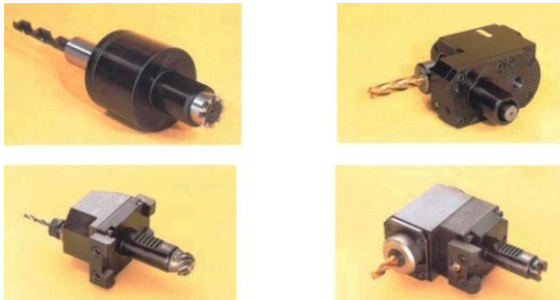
Приводний інструмент для верстатів токарної групи з ЧПУ
